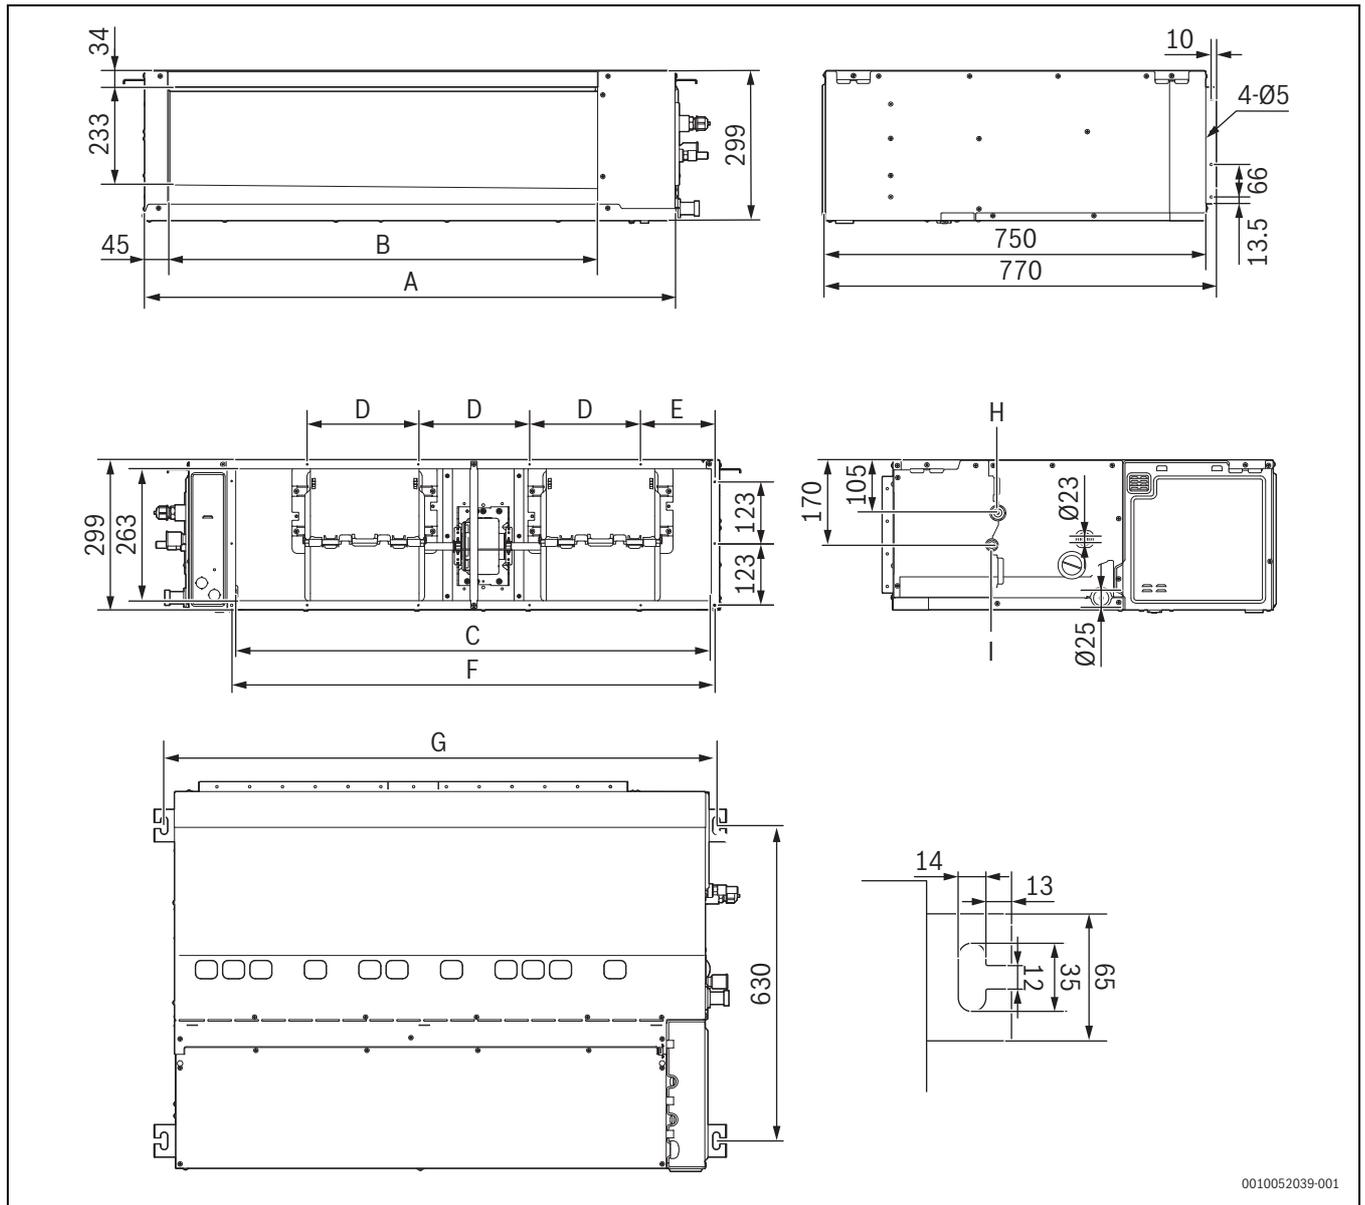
Габаритные размеры и размеры выпускного отверстия (единица измерения мм)
